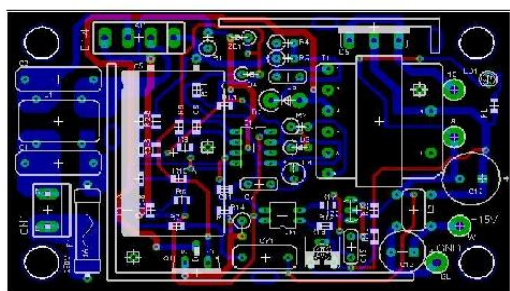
Ejemplo de diseño de PCB para fuente conmutada DC de 50 W
